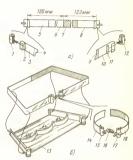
Подготовка тросика сервопривода индикаториой пленки и регудировки громкости:
